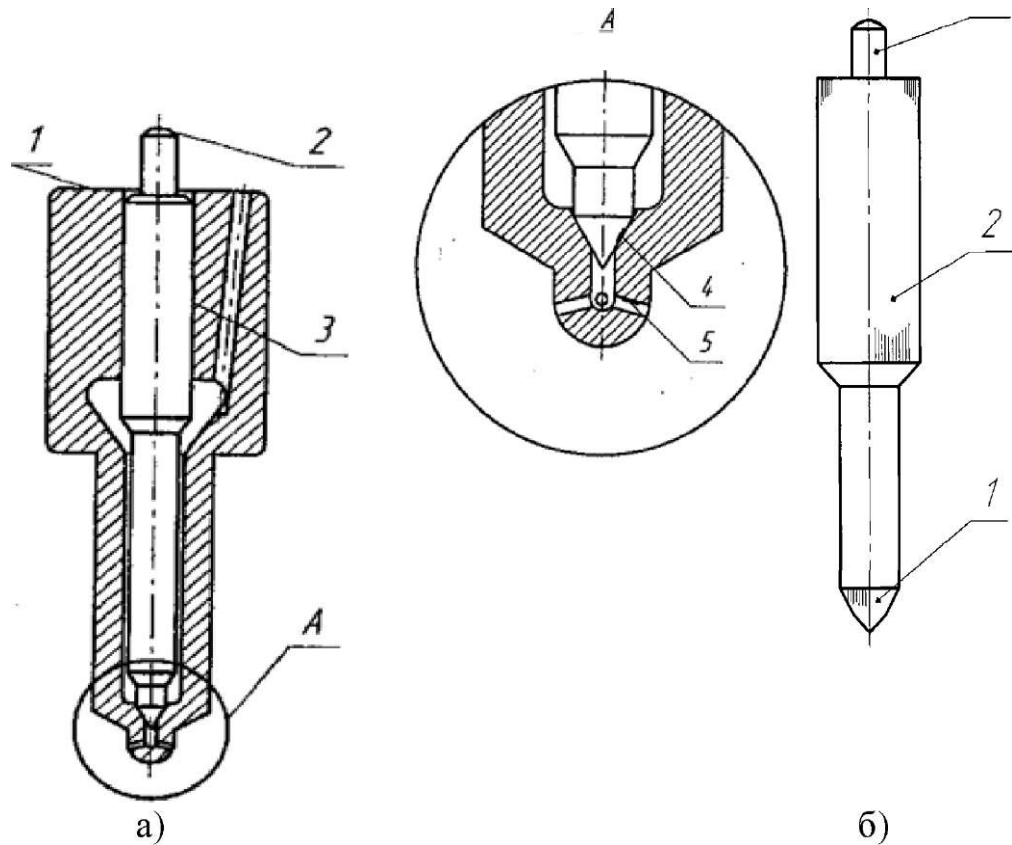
Місця спрацювання робочих поверхнь форсунки: а) розпилювача: 1 - торець корпуса розпилювача; 2 - торець хвостовика голки; 3 - напрямна поверхня корпуса розпилювача; 4 - запірний конус корпуса розпилювача; 5 - соплові отвори; б) голки розпилювача: 1 - запірний конус голки розпилювача; 2 - циліндрична направляюча поверхня голки розпилювача; 3 - хвостовик голки розпилювача.
